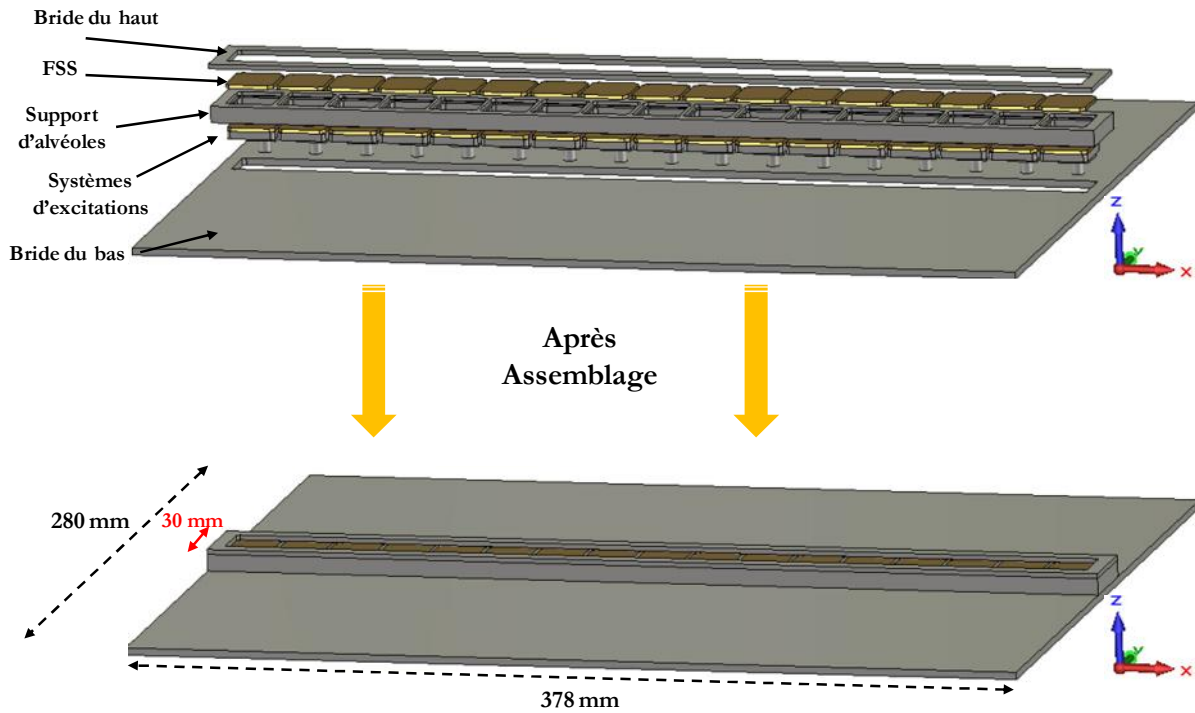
Le modèle du prototype antennaire complet : pièces principales et dimensionnement.
